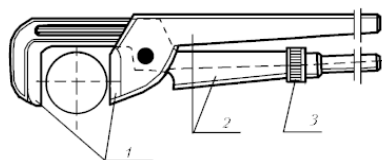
Рычажный трубный ключ «Бако» для отвинчивания контргайек, фланцев, муфт соединительных: 1 – губки зажимные; 2 – ручки-рычаги; 3 – регулятор зажима губок
